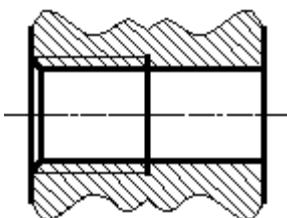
Изображение фаски в отверстии с цилиндрической резьбой
